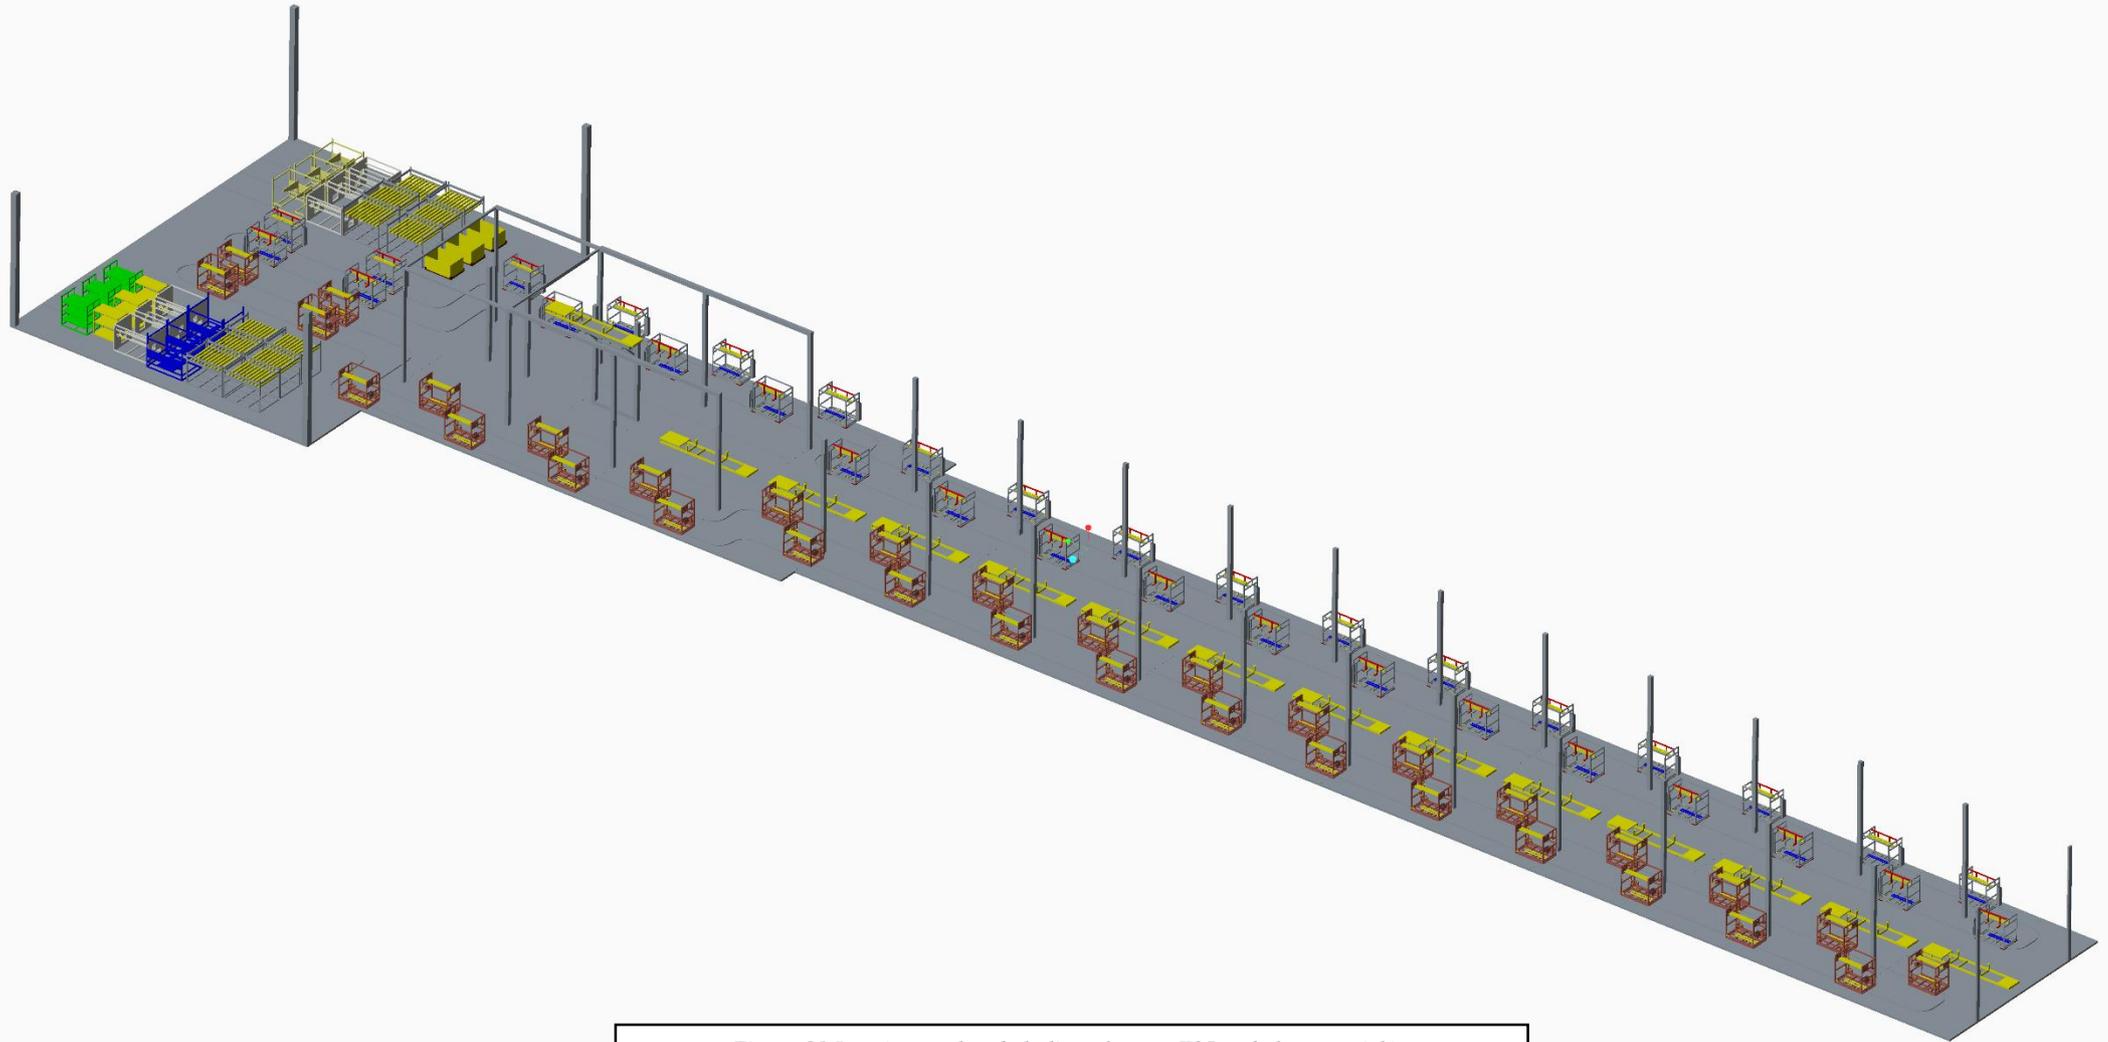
La mise en plan de la ligne ferrage T35 et de la zone picking
